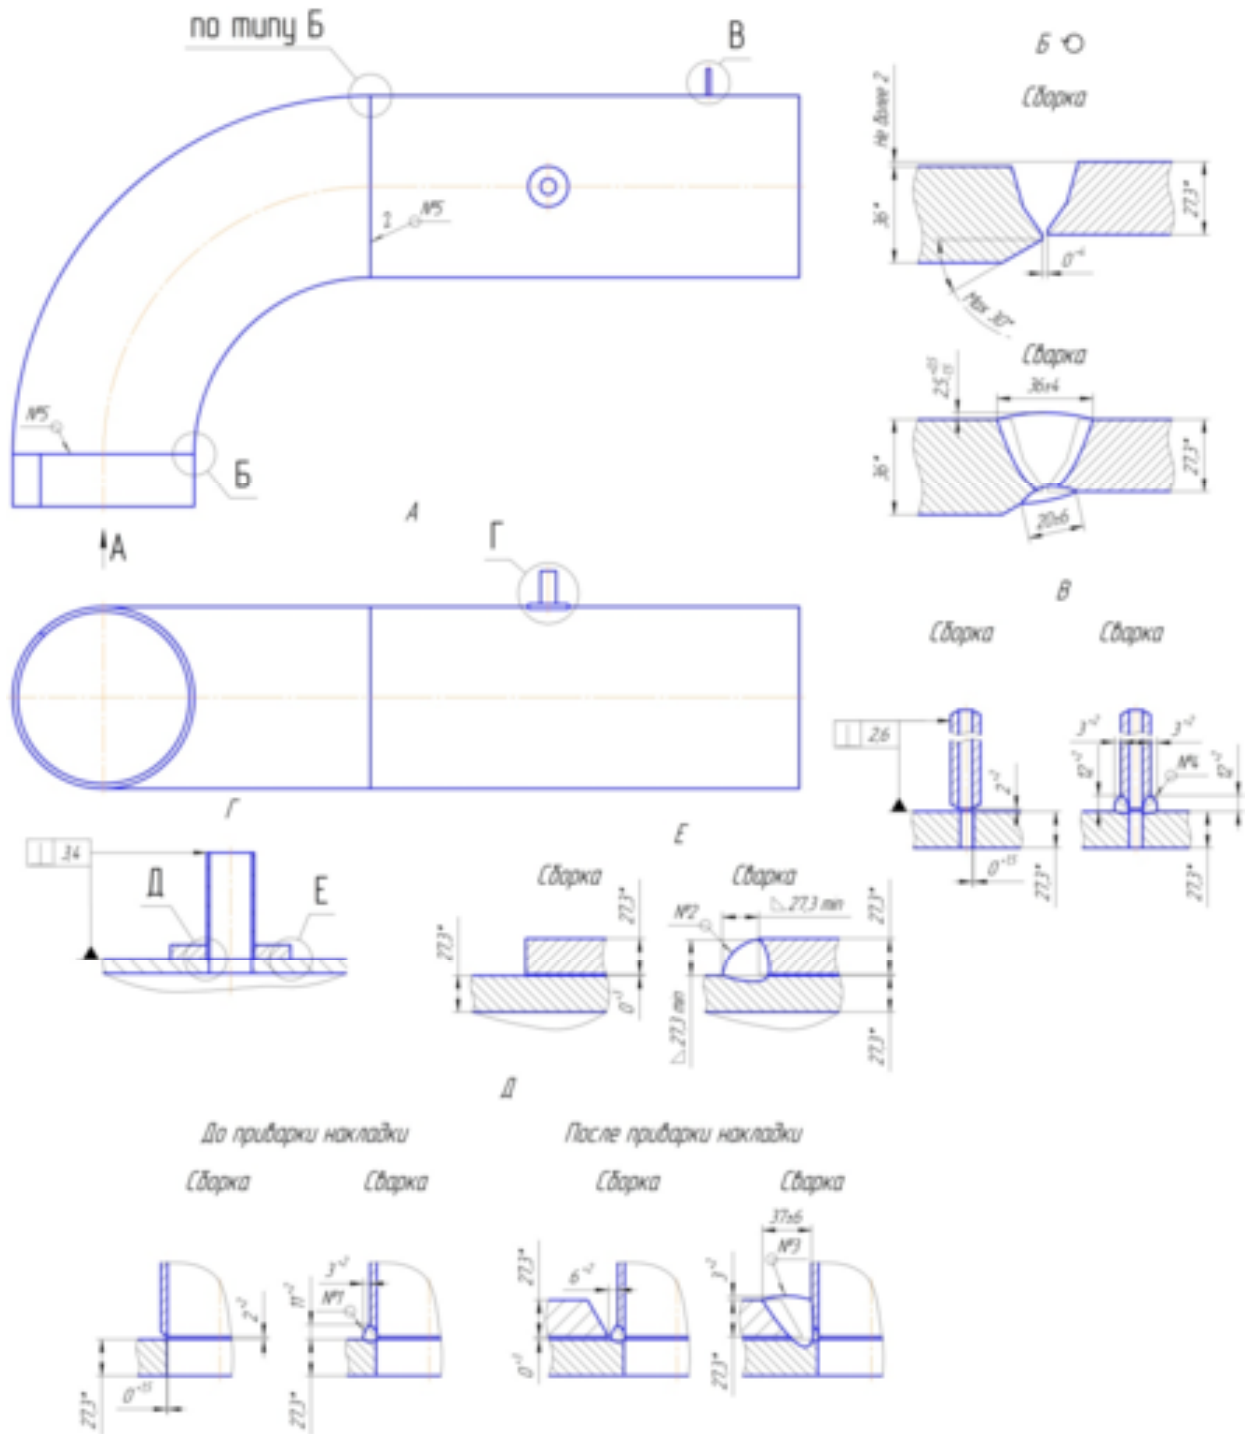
Схема расположения и вид сварных швов
